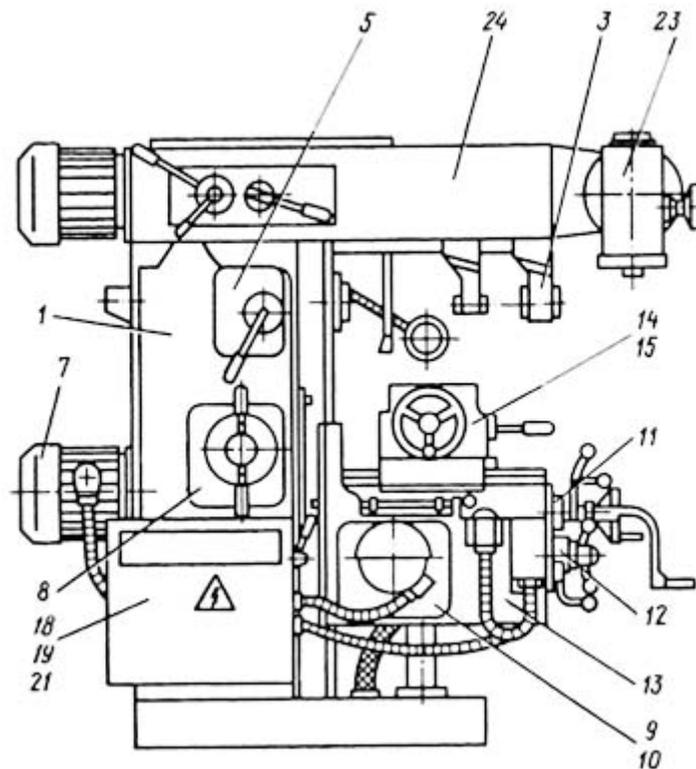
Составные части горизонтального консольно-фрезерного станка 6P81.
